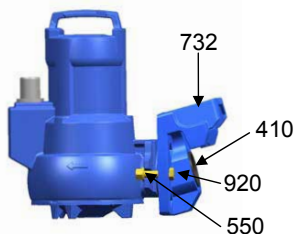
Установка крепеж-захвата при наличии 2 штанговых направляющих
